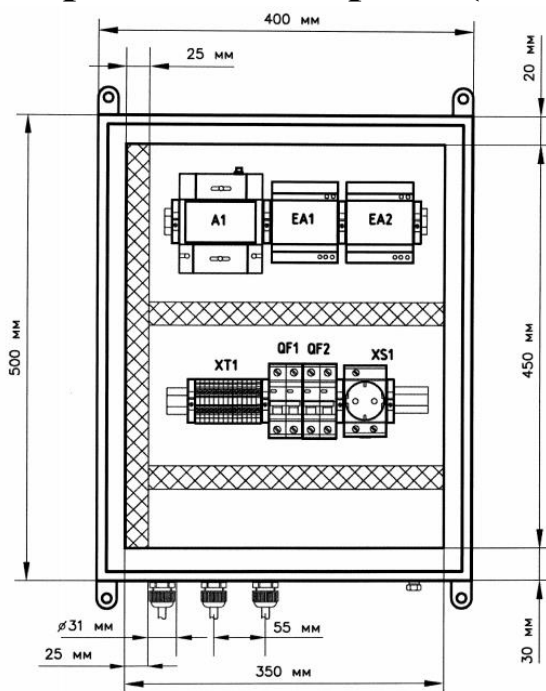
Общий вид (внутренний) и габаритные размеры шкафа АСКУЭ-1-У1.
